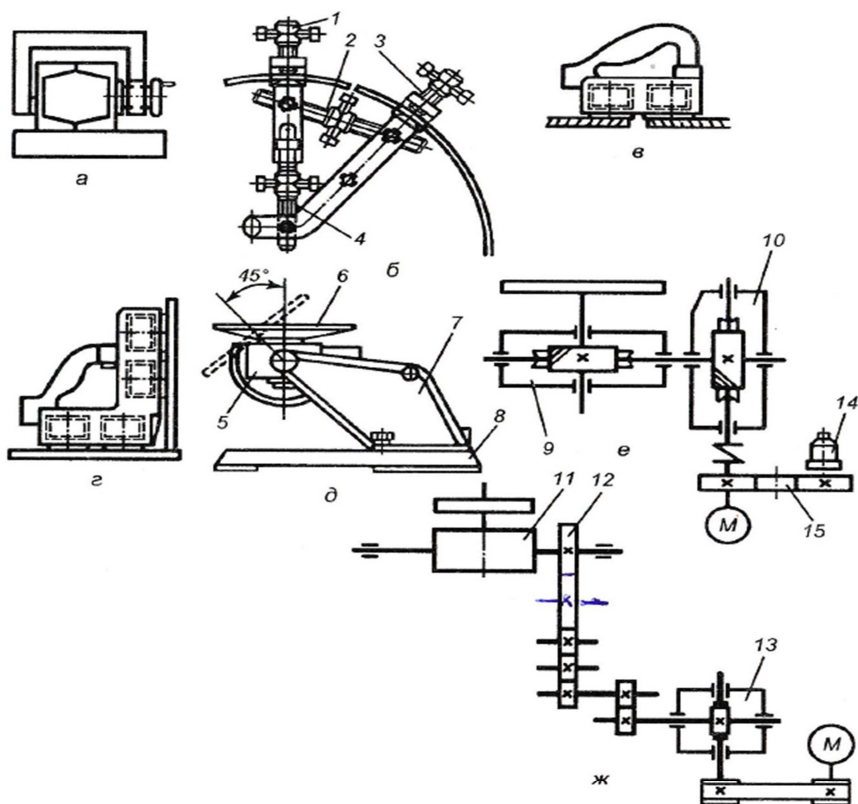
Переносные приспособления и стационарное оборудование для сборки сваркой:
